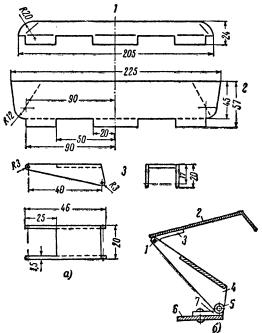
Детали декоративного щитка (a) и сборка шарнирного узла (b).
